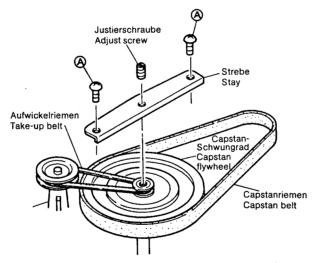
Capstan- und Aufwickel-Riemen Fig. 3-21 Capstan and take-up belt replacement
